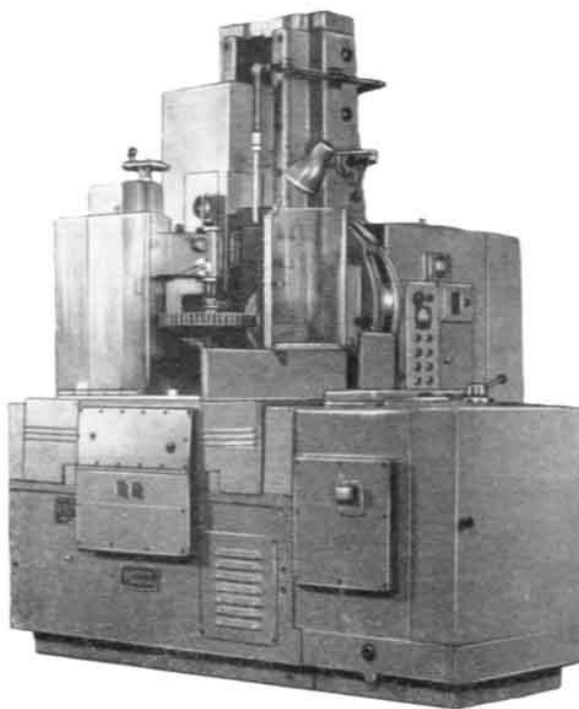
Полуавтоматический зубошлифовальный станок 5841
